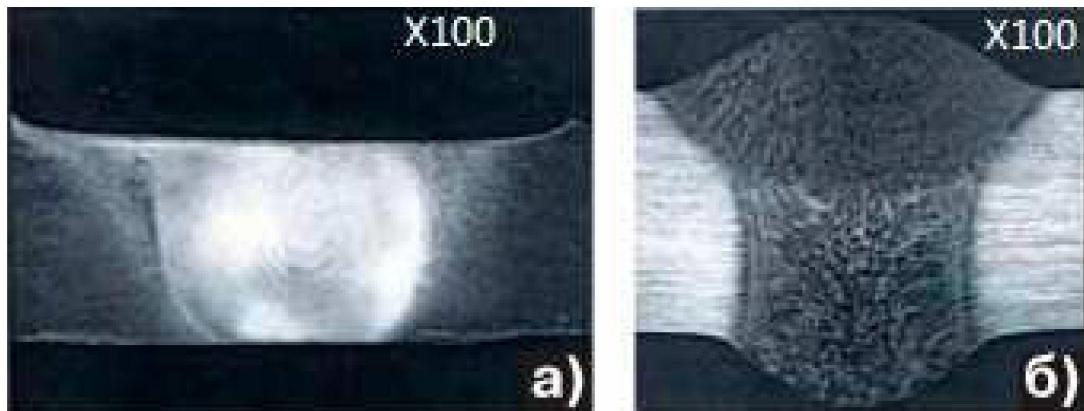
Сечение швов, полученных сваркой трением с перемешиванием (а) и с помощью электродуговой аргоновой сварки (б)
